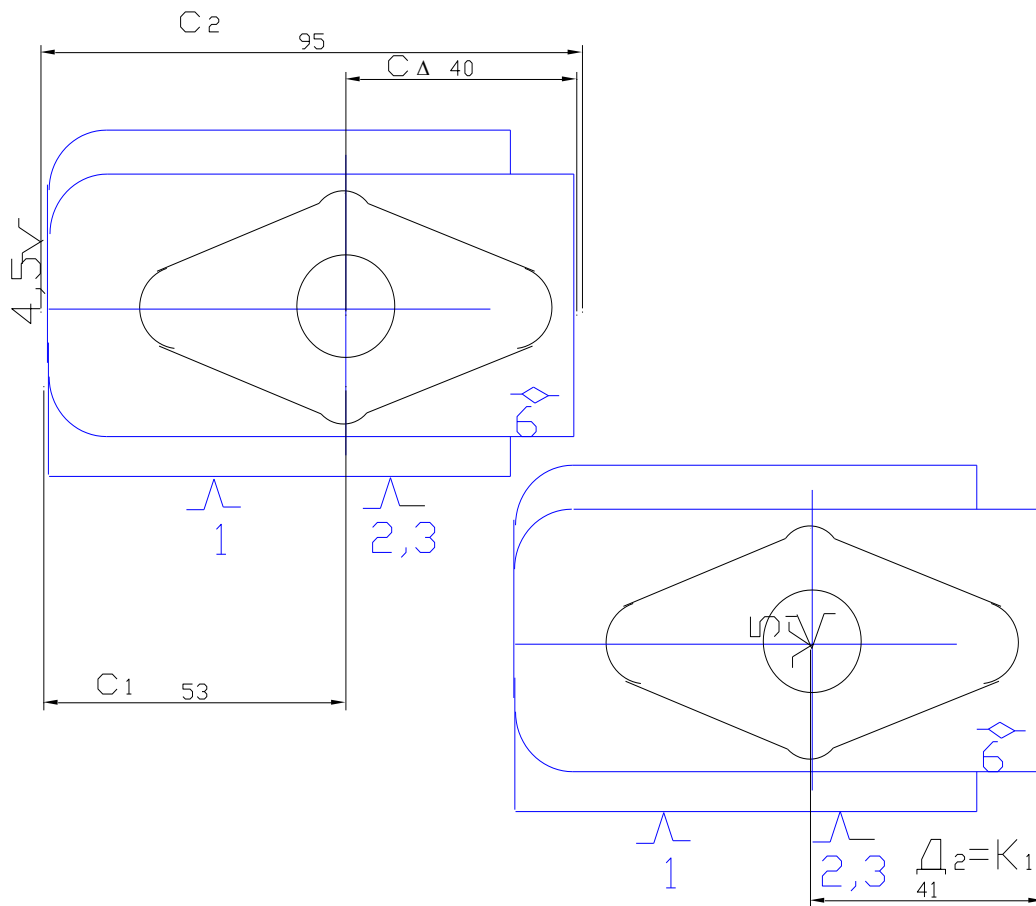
Варіанти базування при обробці установочних поверхонь
